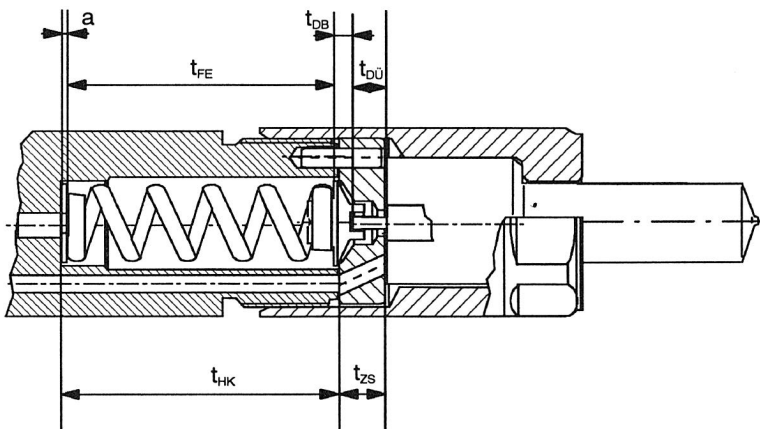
Längentoleranzkette für die Düsenhaltermontage
